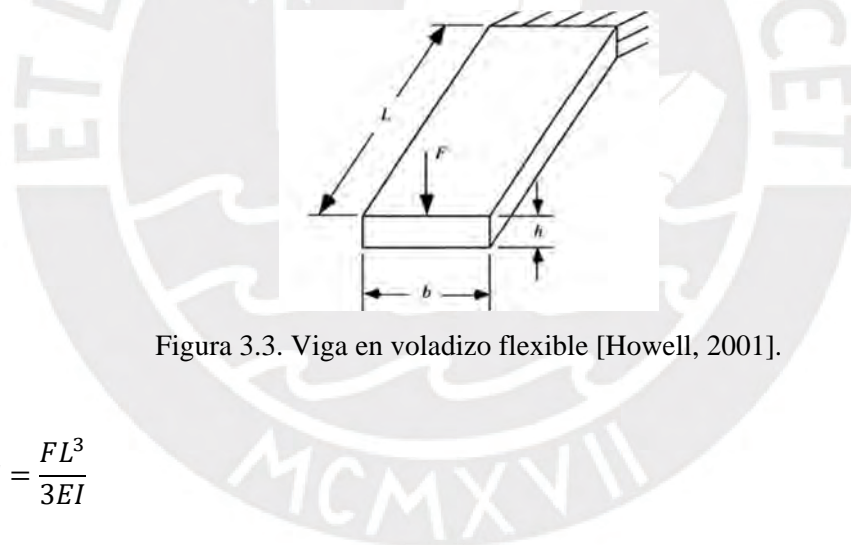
Viga en voladizo flexible [Howell, 2001].
